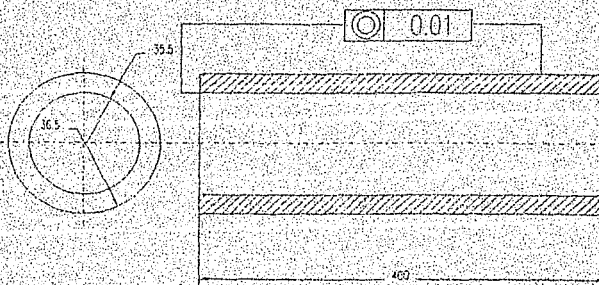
Dibujo de taller del cilindro de aluminio.
